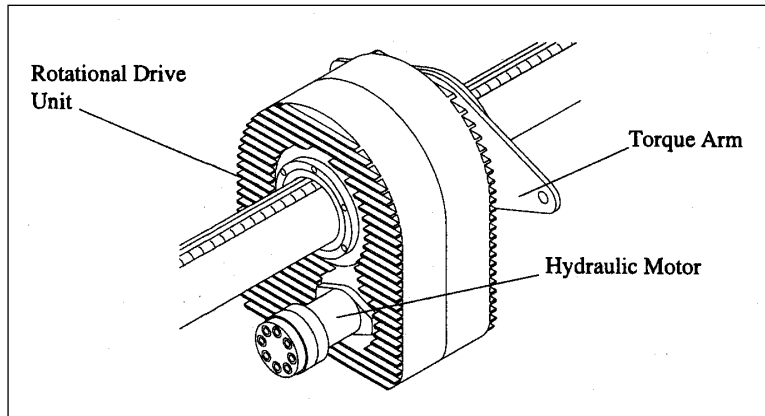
Montage du moteur hydraulique et des barres de torsion sur le RDU
